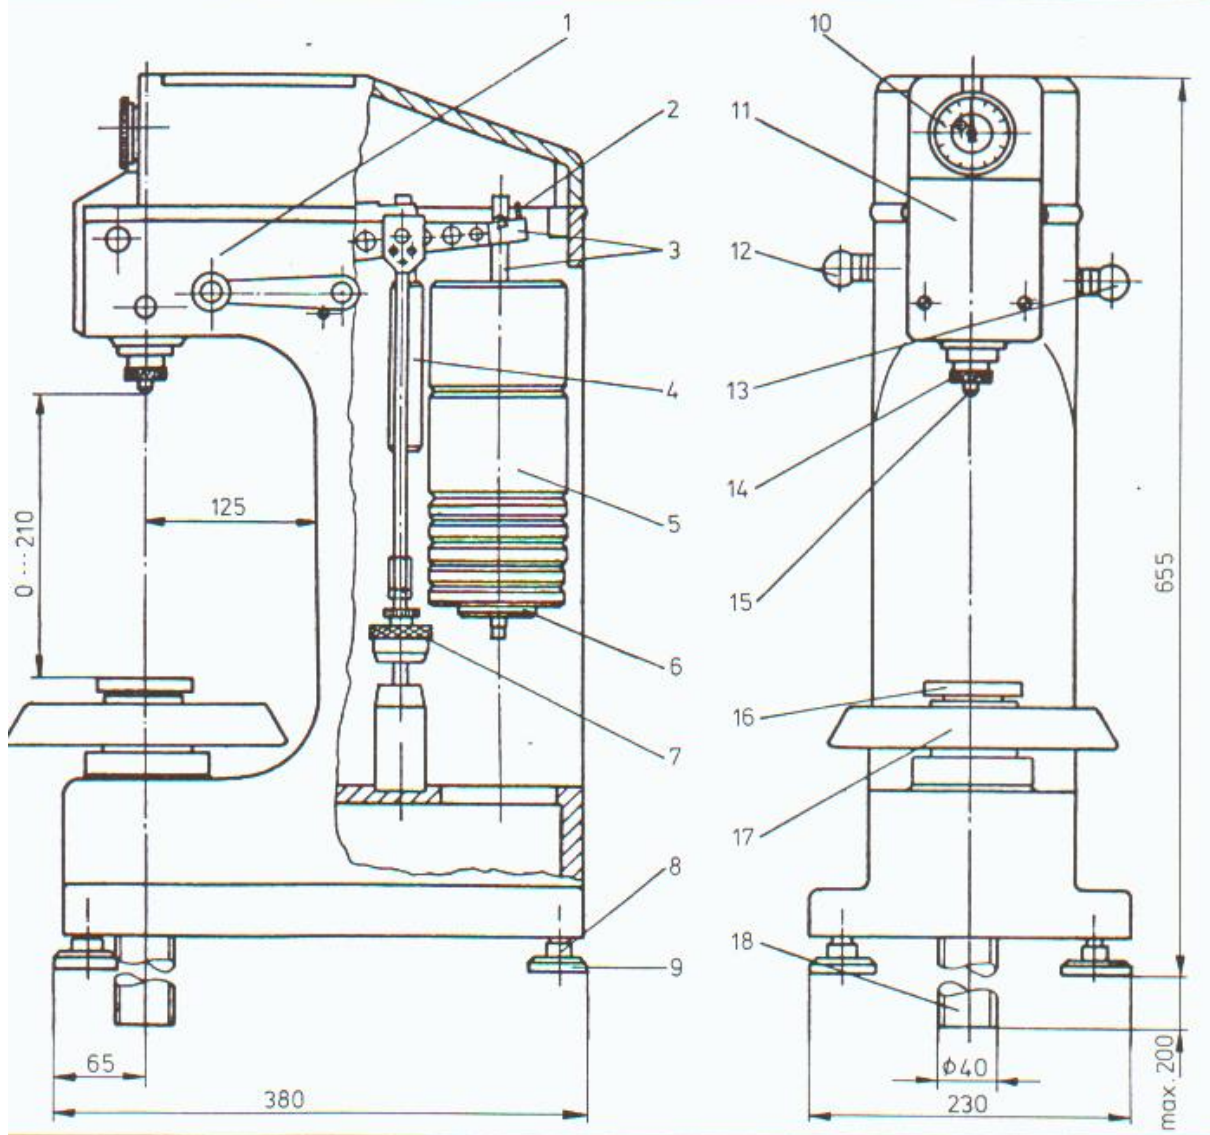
Aufbau der Werkstoff-Prüfmaschine Zwick 3106 B
